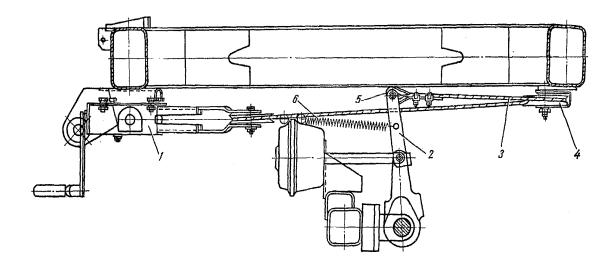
Привод стояночного тормоза: 1 — натяжной мехянизм; 2 — рычэг приводной; 3 — трос; 4 — ролик; 5 — коуш; 6 — пружина возвратная
